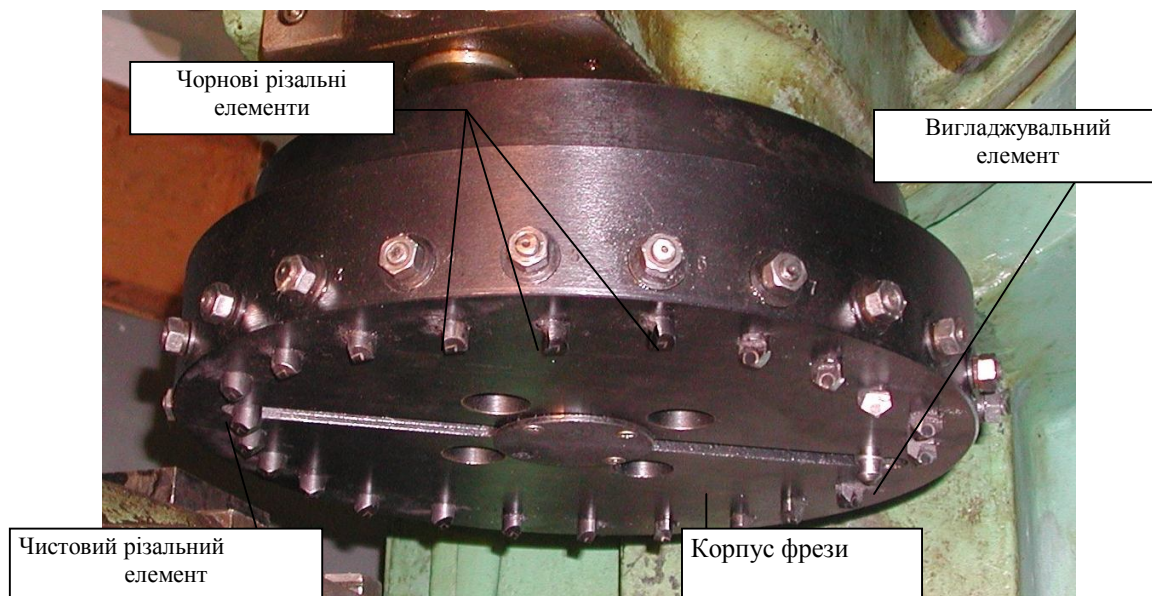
Загальний вигляд торцевої фрези з рухомими елементами
